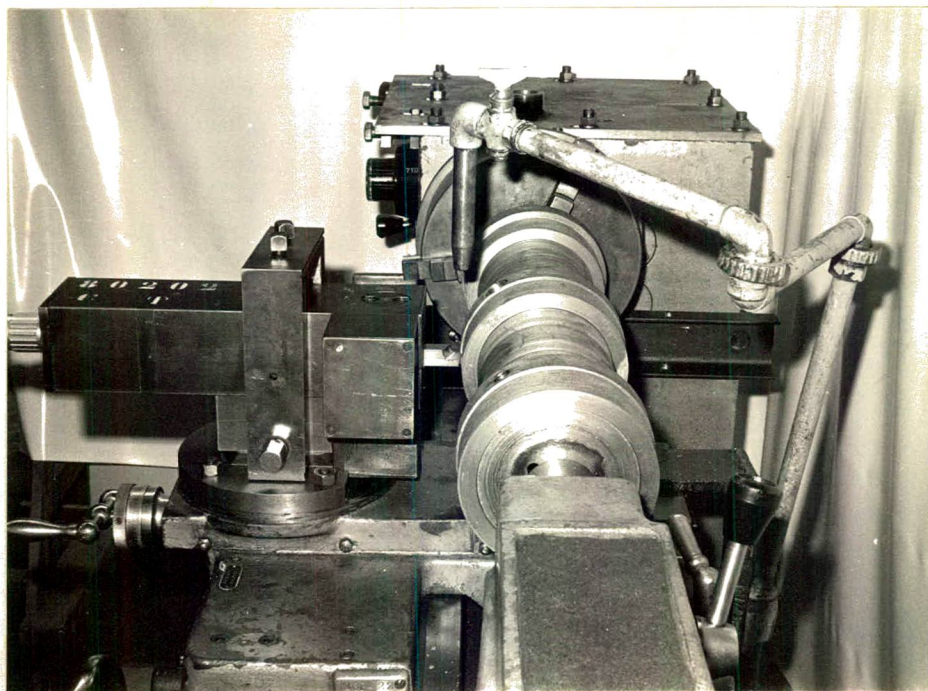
Detalhe da usinagem através do dinamômetro Fischer.
